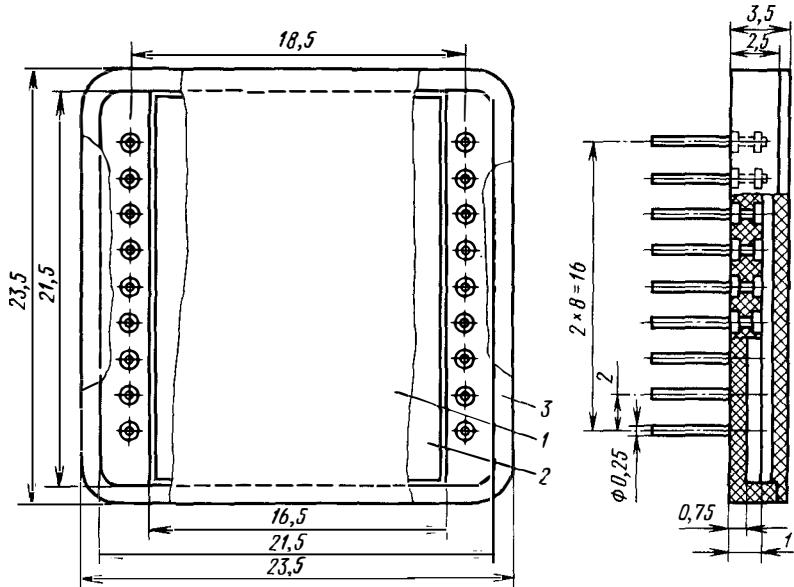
Полый полимерный корпус со штыревыми выводами:
